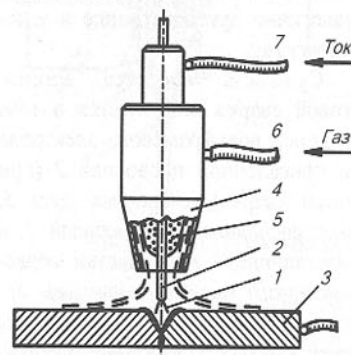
Схема сварки в углекислом газе
